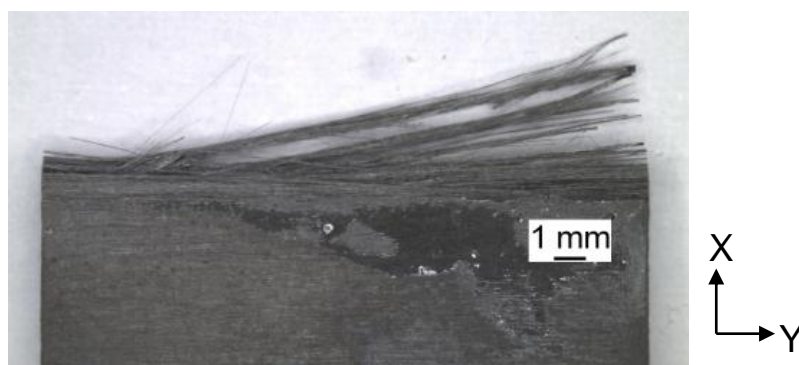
Photo d'une éprouvette courbe de composite carbone/époxy bobiné rompue.
